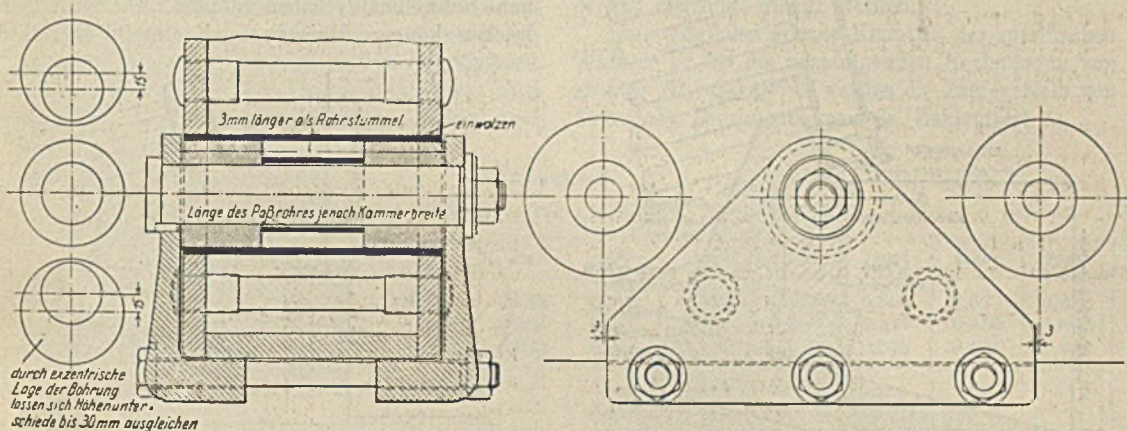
Vorrichtung zur Sicherung der Schweißnähte von Wasserkammern.
